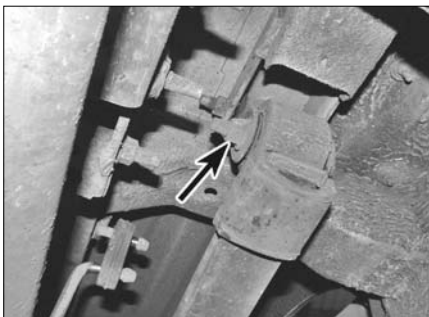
,б. ...и гайка заднего болта крепления задней рессоры
